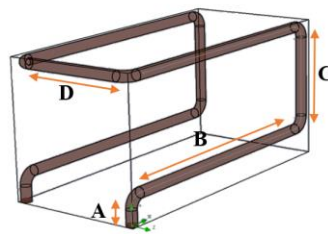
19 Dimensionamiento del serpentín de cobre. [Autor]
